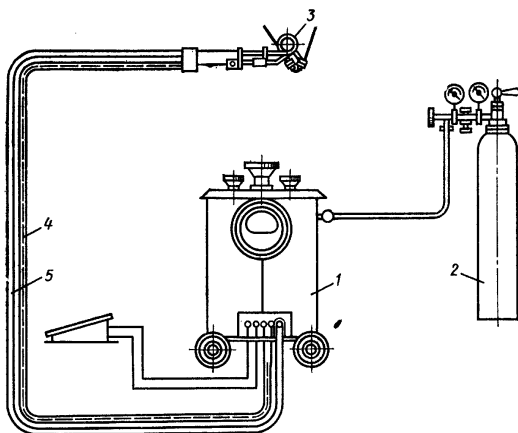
Схема установки для атомно-водородной сварки:
